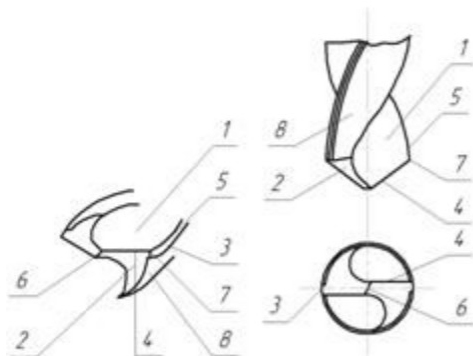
Поверхности лезвий сверла и его режущие кромки
